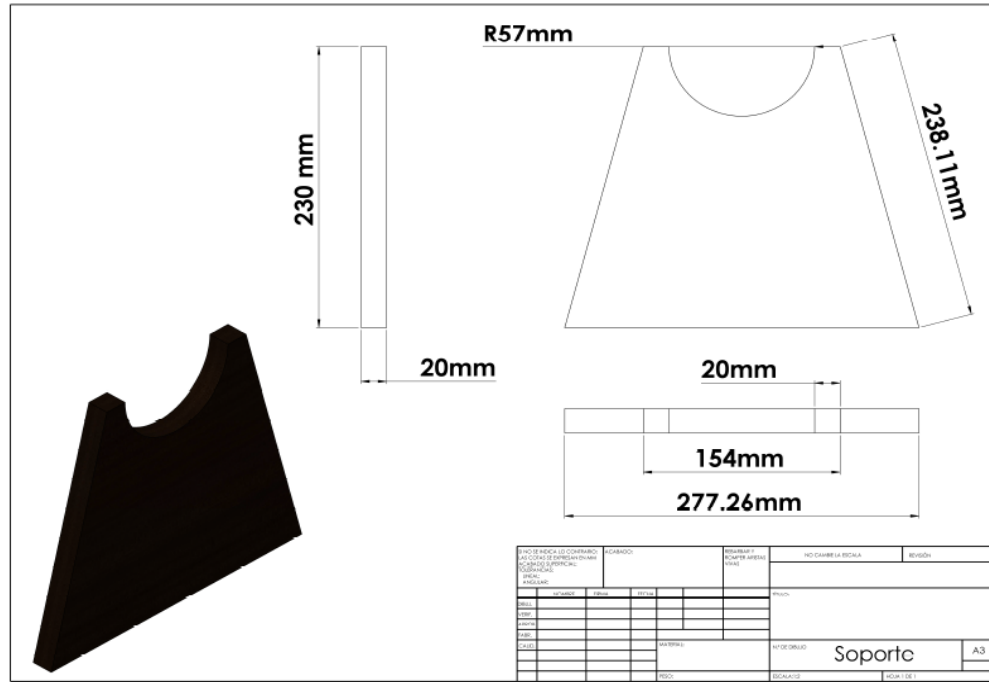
Plano de Soporte del intercambiador de tubos y coraza, Fuente Solidworks 2014
